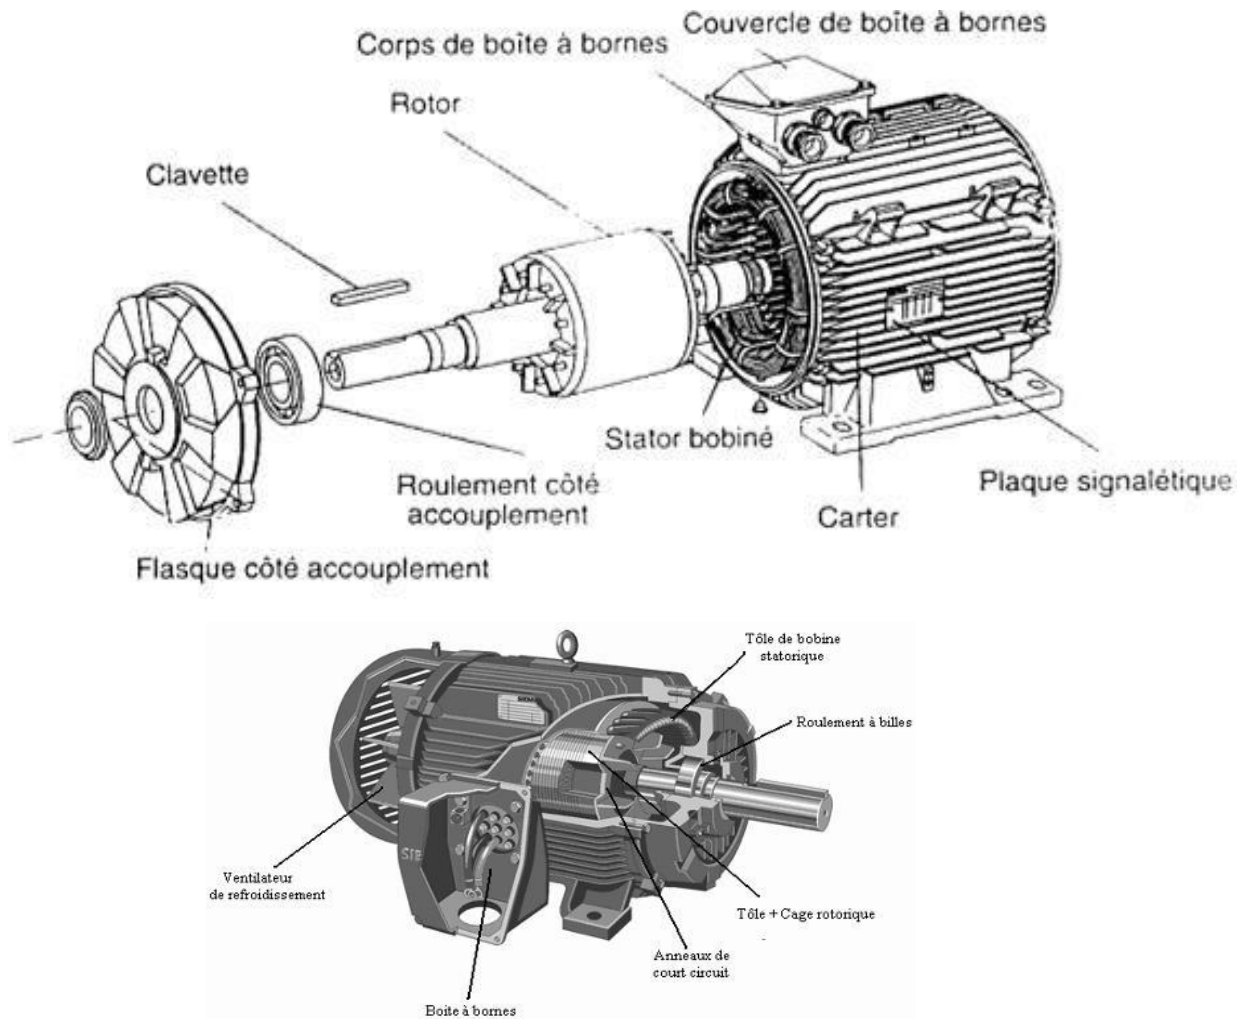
Vue éclatée d'une machine asynchrone double étoile [19].
